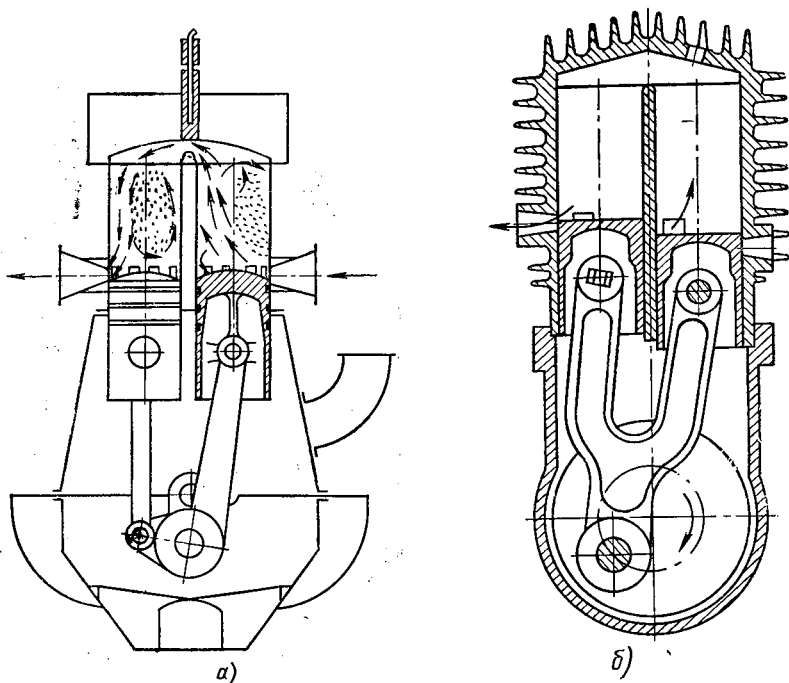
Схемы двигателей с параллельным расположением цилиндров и общей камерой сгорания
